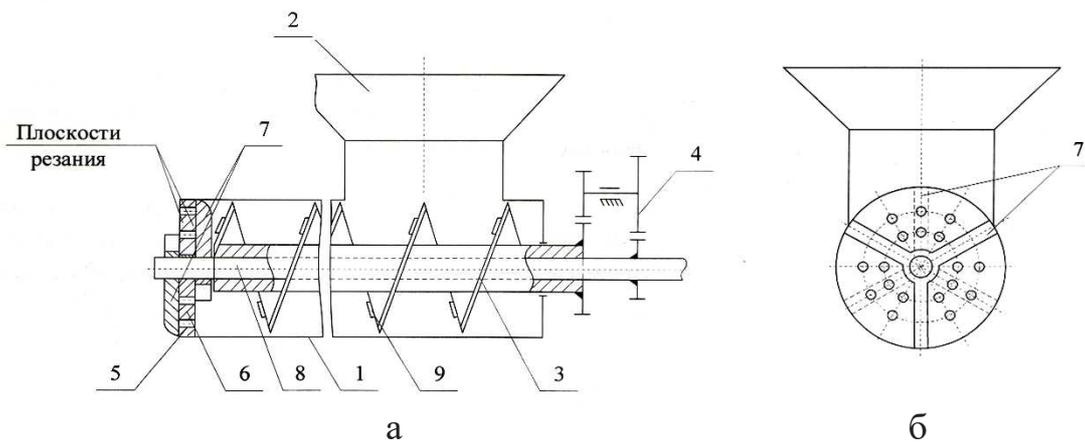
Схема измельчителя коры: а – вид спереди; б – вид слева
